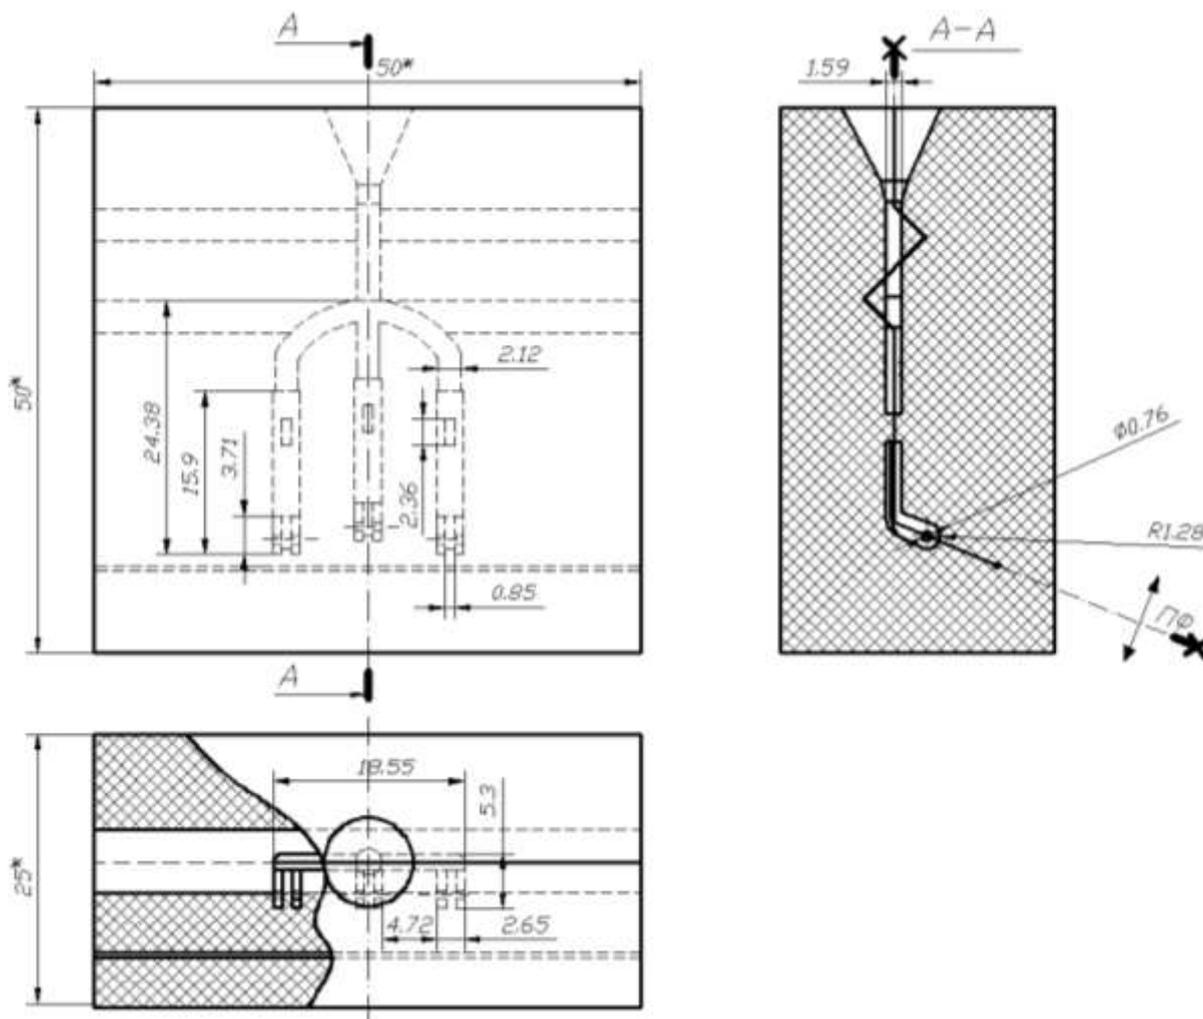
Резиновая пресс-форма для получения восковой модели отливки «блок - швенза»
